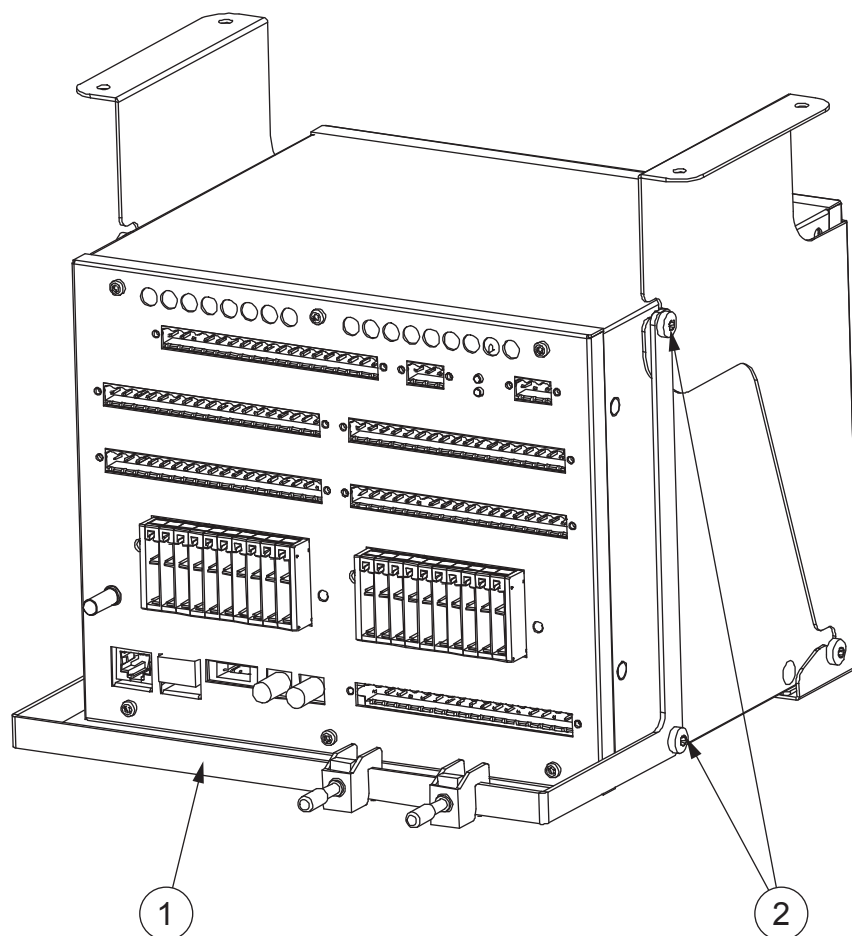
4U de mitad de 19" Montaje del raíl de sujeción del cable opcional
